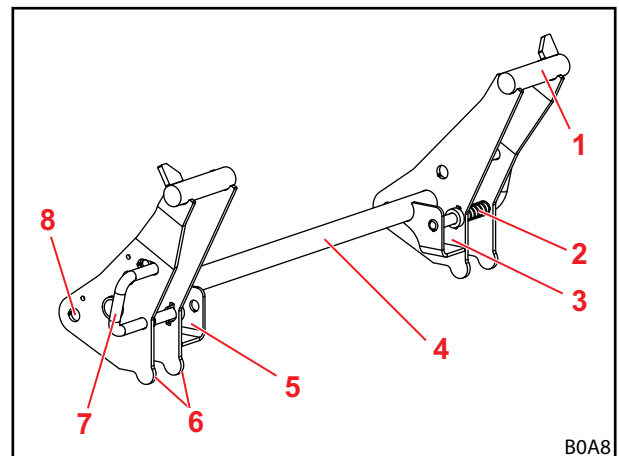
Werkzeug-Verriegelung am Euro-Wechselrahmen
